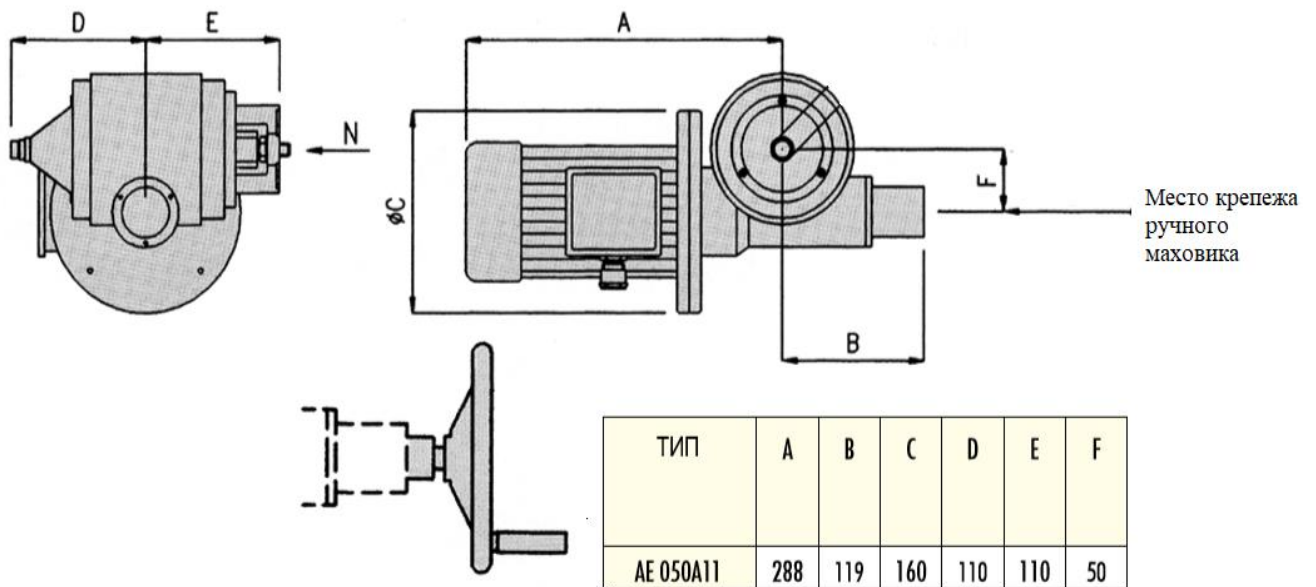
Габаритные размеры электродвигателя с редуктором и крепление маховика к редуктору
